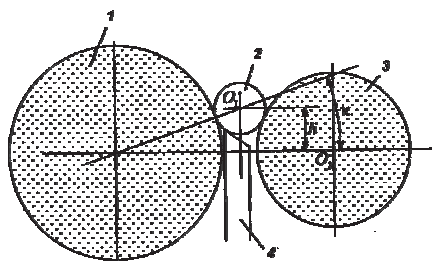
Схема установки центра заготовки над линией центров шлифовального и ведущего кругов: 1 – шлифовальный круг; 2 – заготовка; 3 – ведущий круг; 4 – нож
